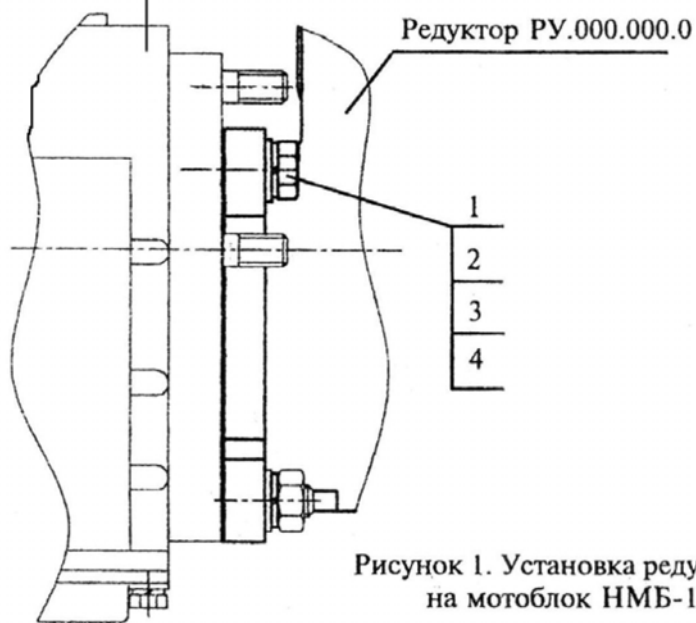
Установка редуктора на мотоблок НМБ-1
